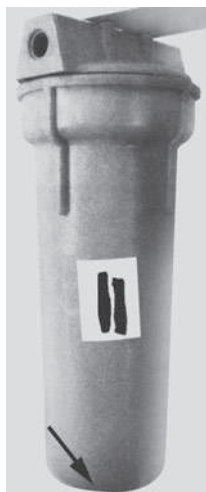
Разрушенный корпус фильтра для воды
